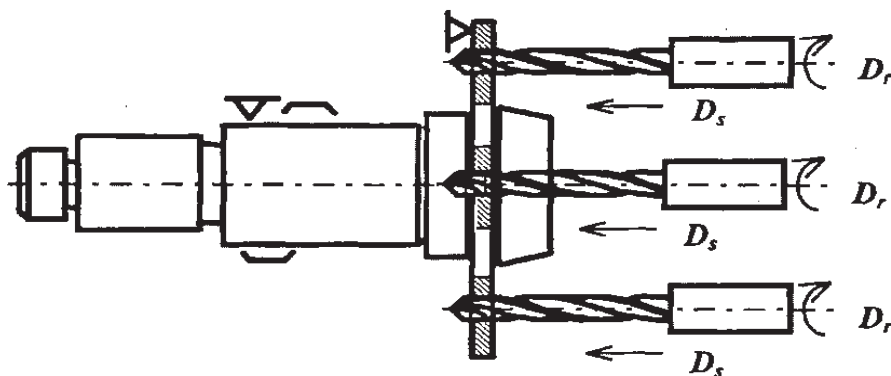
Схема обработки внецентровых отверстий на агрегатном станке
